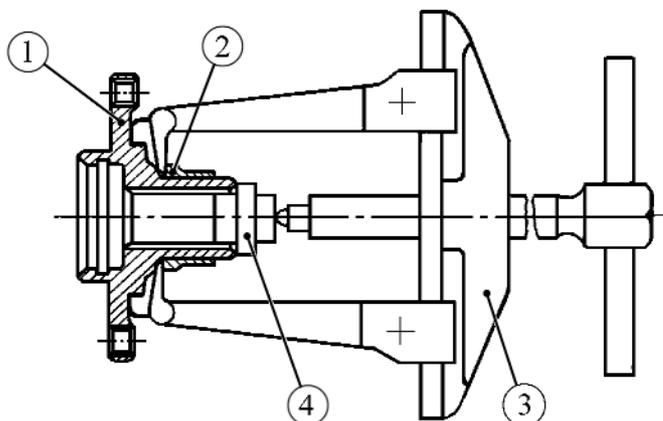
Спрессовка внутреннего кольца подшипника со ступицы переднего колеса:
